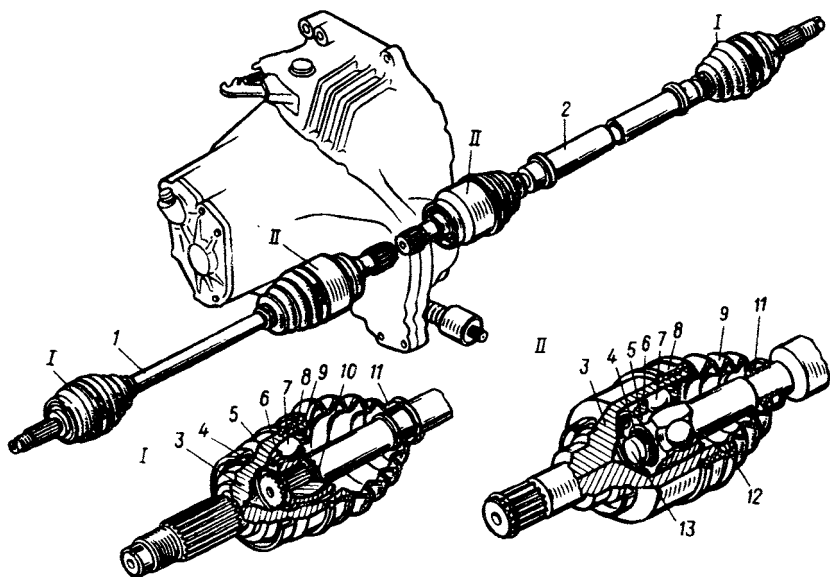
Привод передних колес автомобилей ВАЗ-2108, -2109:
